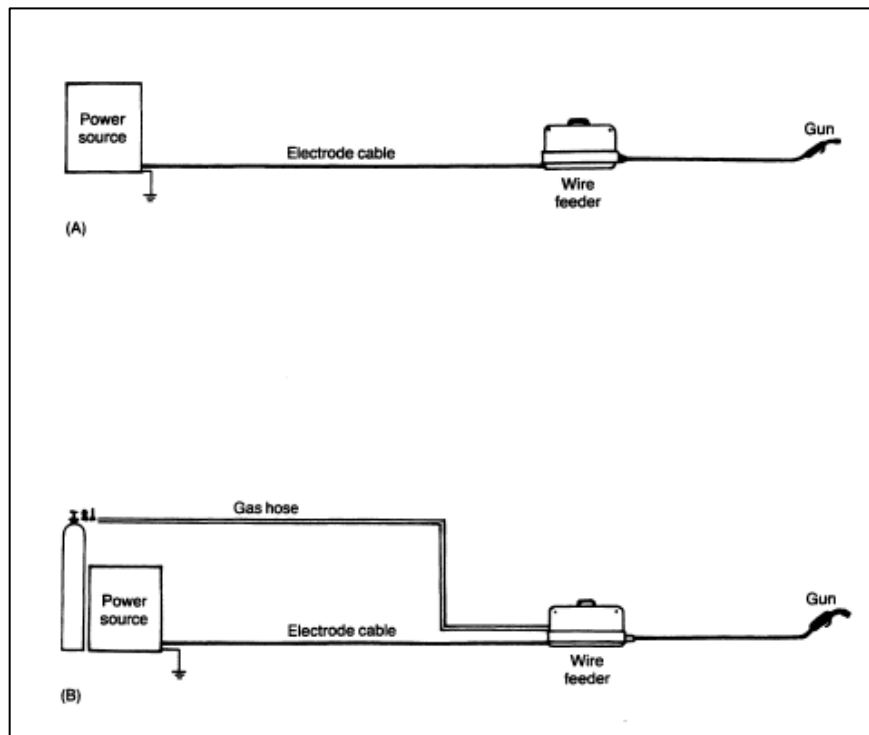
Exemplos de processo de soldagem por (a) “*self-shielded*” e (b) “*gas-shielded*” (11)
